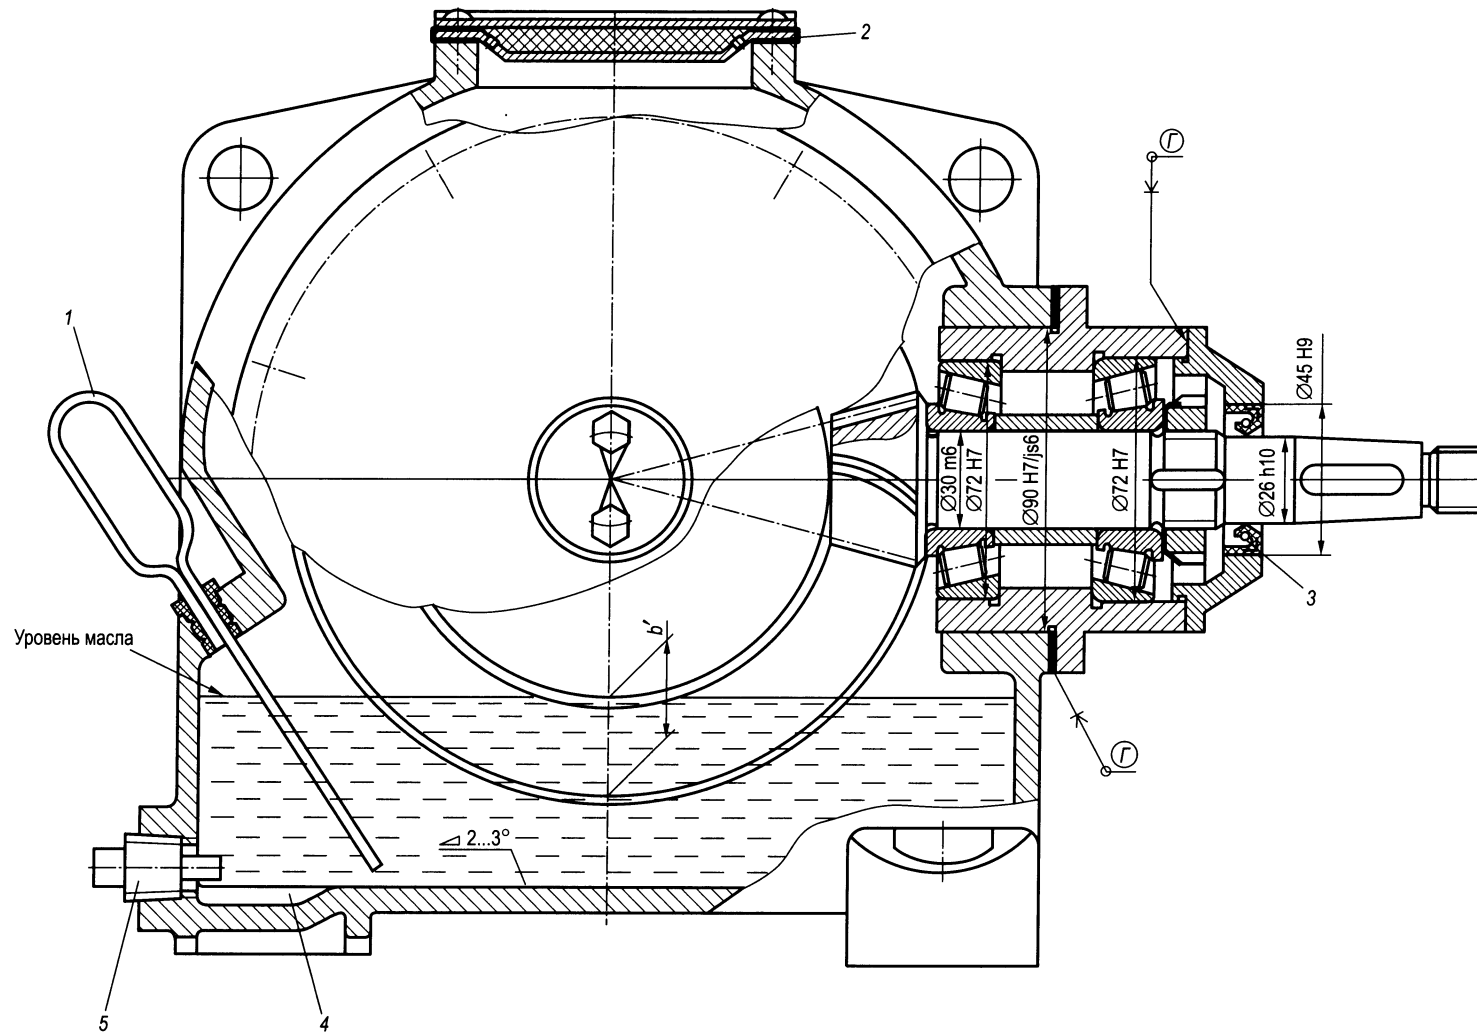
Конический редуктор с погружением колеса в масляную ванну на всю ширину b' зубчатого венца:
